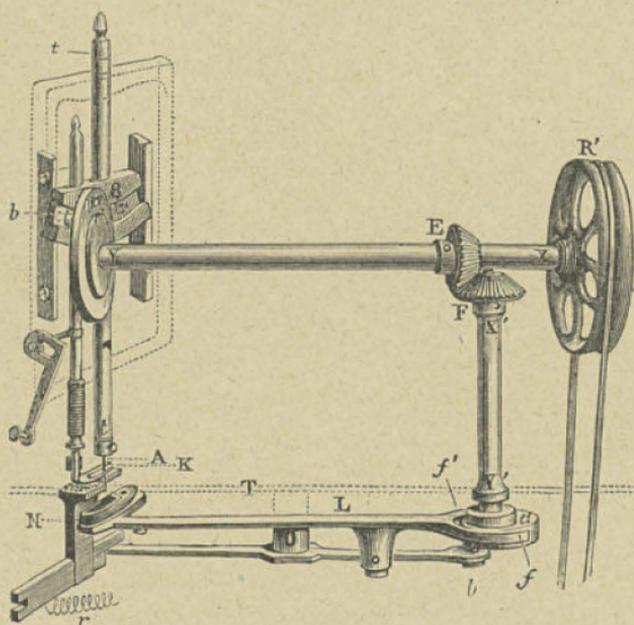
Mécanisme d'une machine à coudre. La poulie R par les arbres E et F fait mouvoir deux excentriques en Y et Y'; l'une fait glisser l'aiguille verticalement, l'autre fait mouvoir la navette horizontalement.
